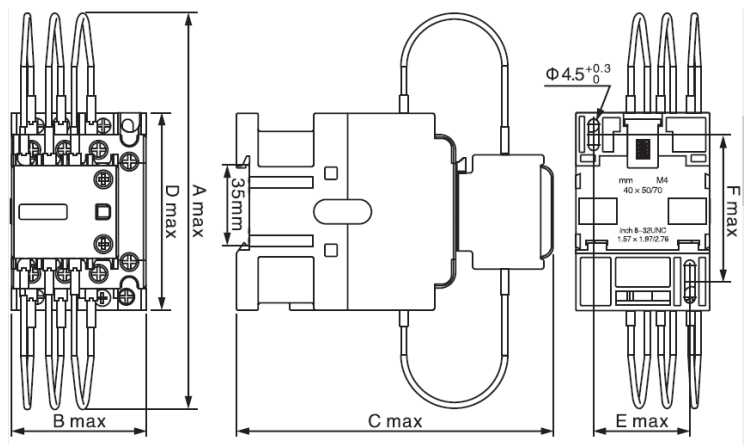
Габаритные и установочные размеры KM-102-CAP 12 ~ 25 кВАр.
